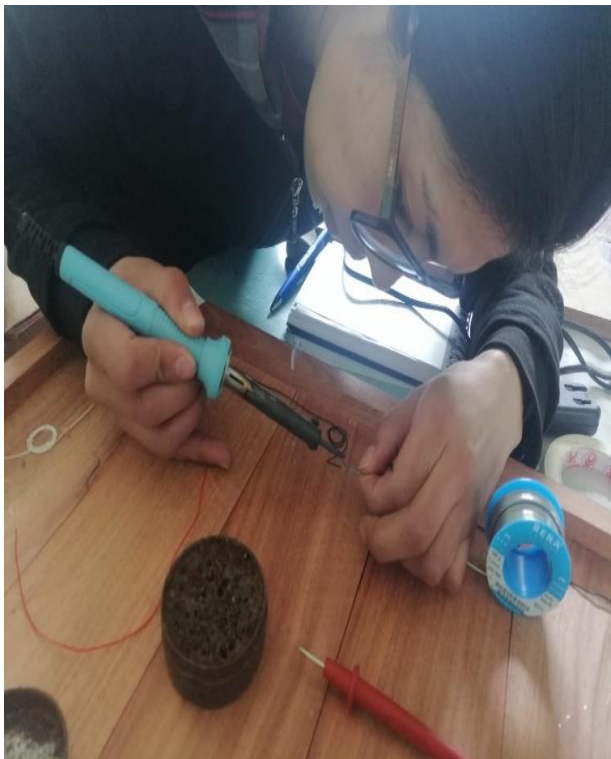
Soldado de cables con estaño de los sensores de peso
